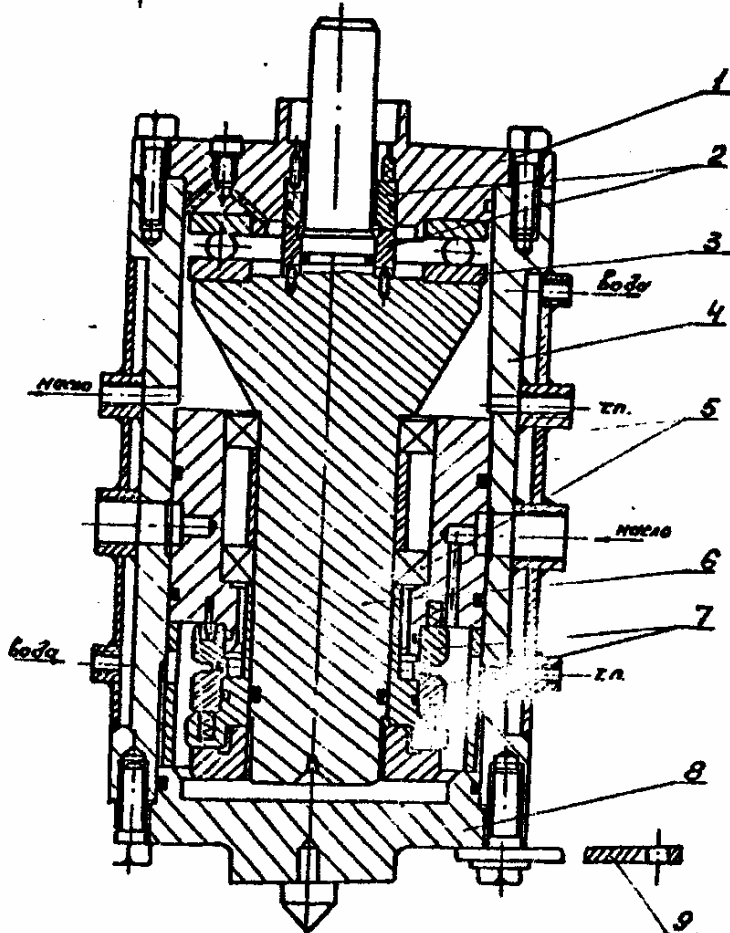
Рабочий узел стенда для испытания торцового уплотнения: 1 – верхняя крышка; 2 – запирающее торцовое уплотнение; 3 – шарикоподшипник; 4 – корпус; 5 – шарикоподшипник; 6 – вал; 7 – торцовое уплотнение; 8 – нижняя крышка; 9 – рычаг.
